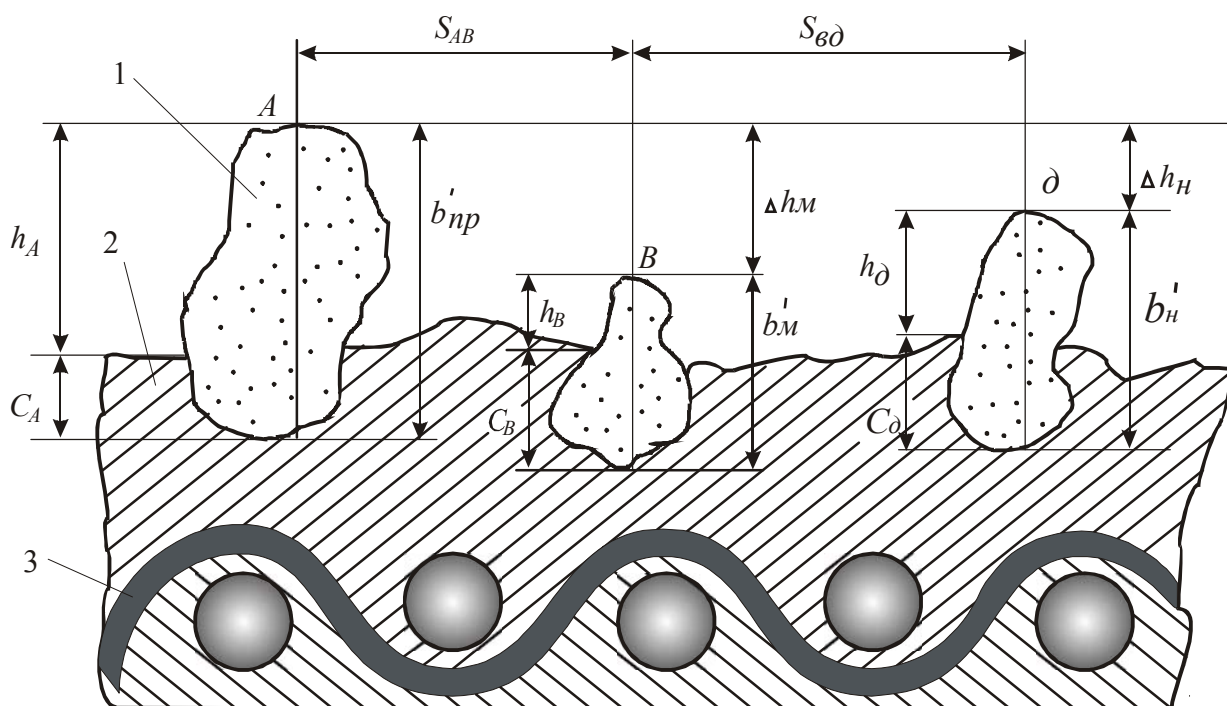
Схема расположения зерен на рабочей поверхности:
